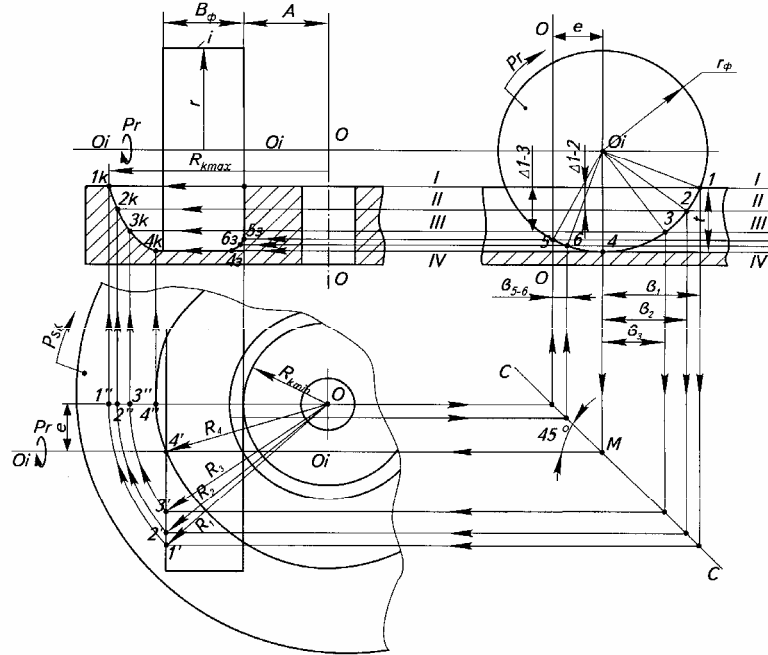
Схема обробки кільцевої канавки дисковою фрезою для випадку зміщення вісі обертання фрези відносно вісі обертання деталі
